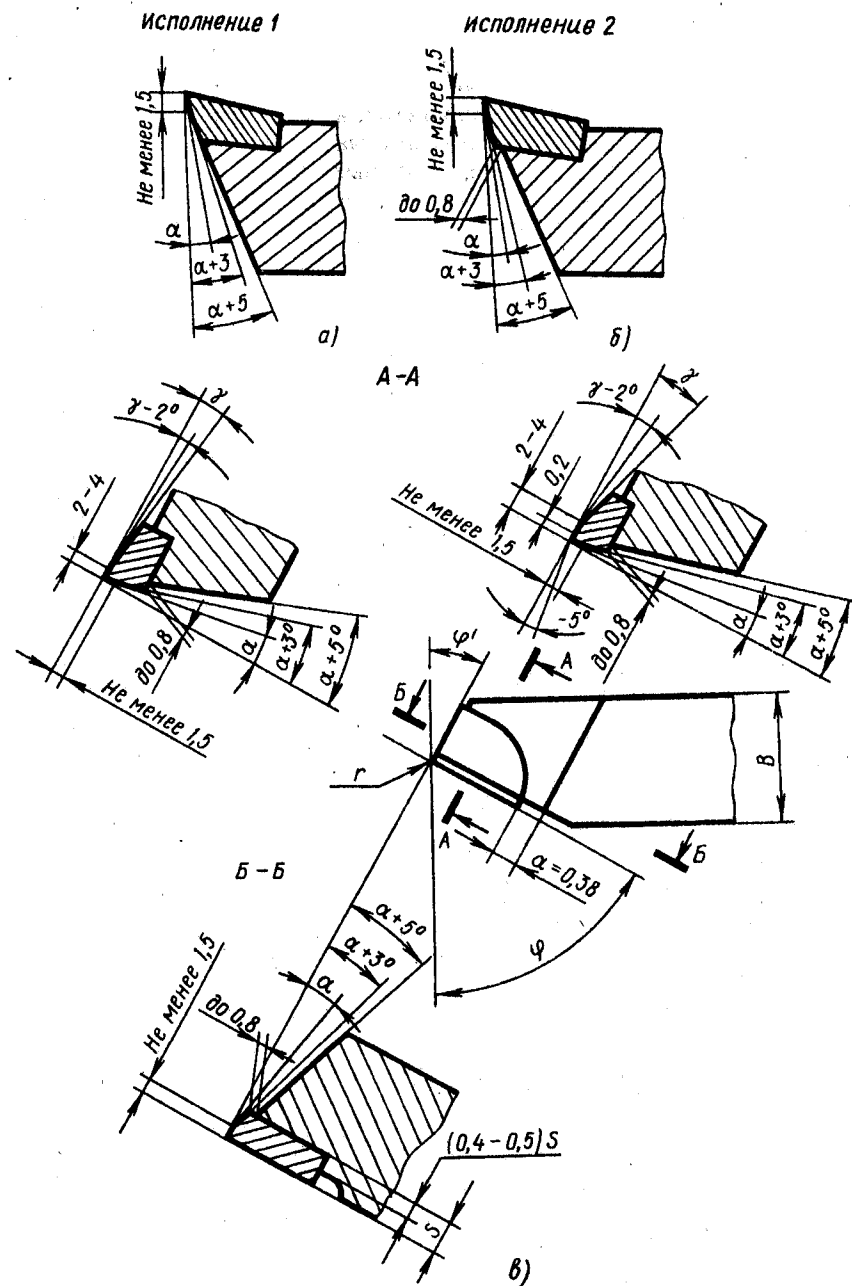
Формы задней поверхности резца с твердосплавной пластинкой, припаянной с разным исполнением
